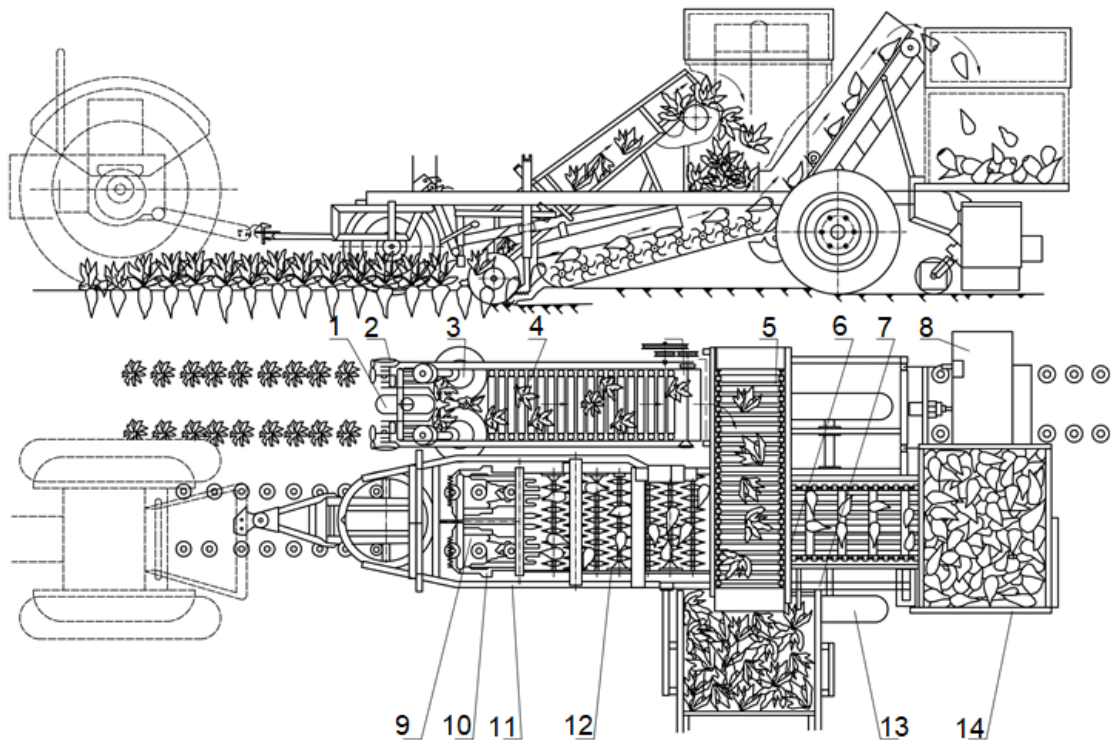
Конструктивно-технологічна схема причіпного комбайна СКН-2: 1 – копіювальне колесо; 2 – пасивний гребінчастий копір; 3 – дисковий ніж; 4, 5 – транспортер гички; 6 – бітер; 7 – перехідна ємність для зрізаної гички; 8 – лопатевий очисник; 9 – копач; 10 – дисковий копач; 11 – рама; 12 – очисник-транспортер вороху; 13 – опорне колесо; 14 – бункер коренеплодів
